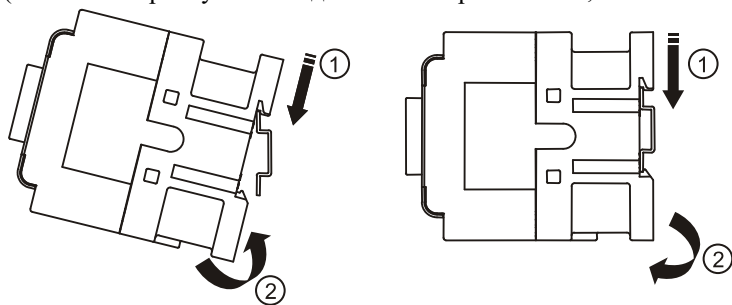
Способ установки /демонтажа контактора на токи 6-38А
